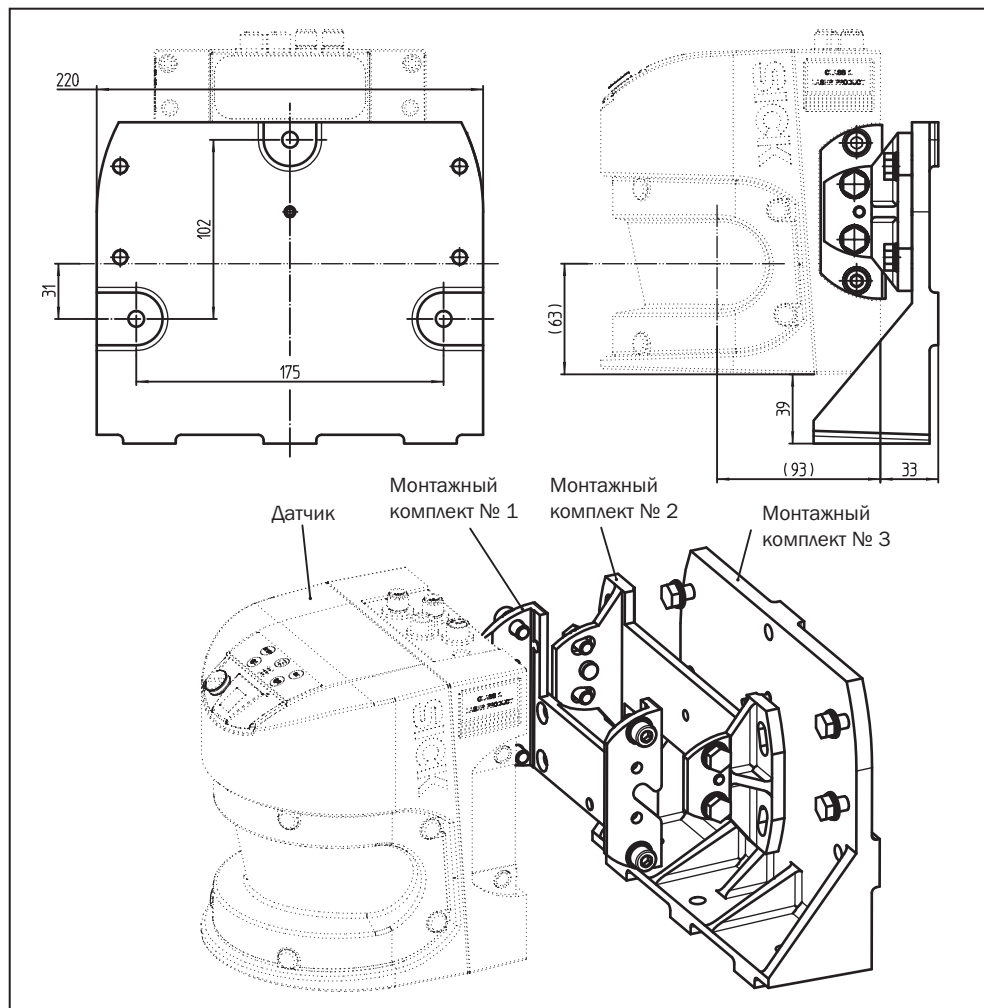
Размерный чертёж монтажного комплекта № 3 (мм)
